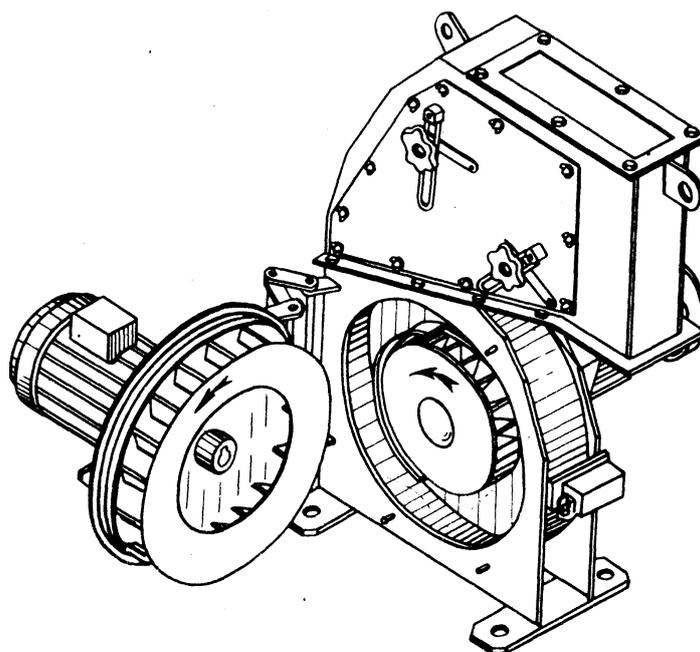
Дробилка зерна ударно-центробежная ДЗУ-Ф-2
